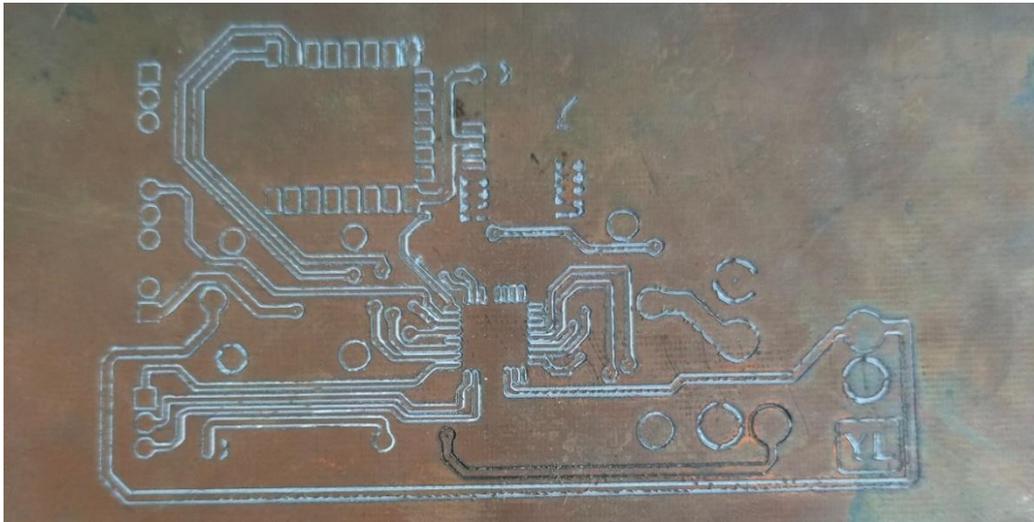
11 Hasil PCB Fiber Fr4
